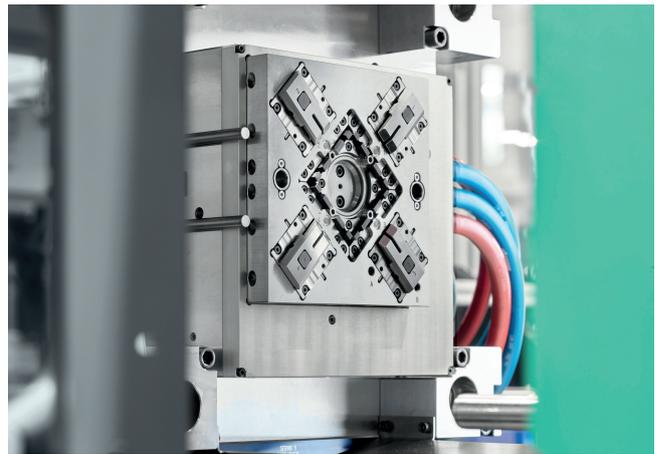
Luer-Konnektoren mit angespritztem Septum am Deckel. Dieser wird mit einem ausgeklügelten Mechanismus noch im Werkzeug geschlossen. © Arburg
